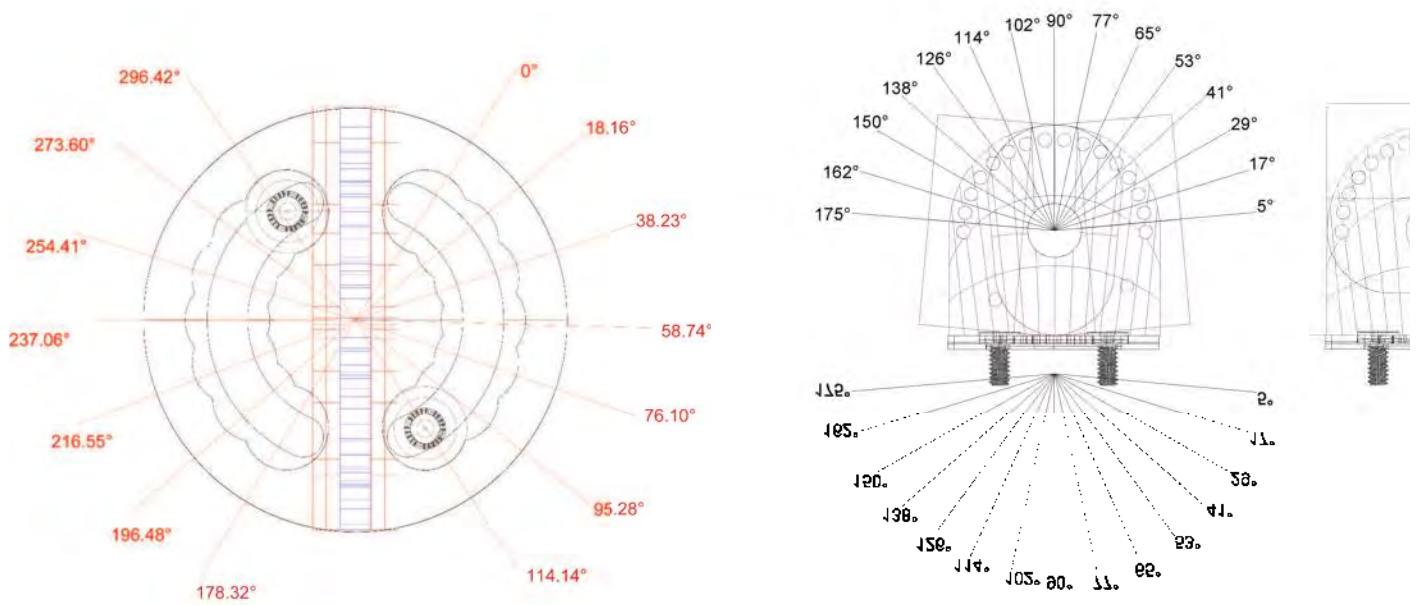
Vista de cabecal de brazo adaptable, en planta y alzado.
